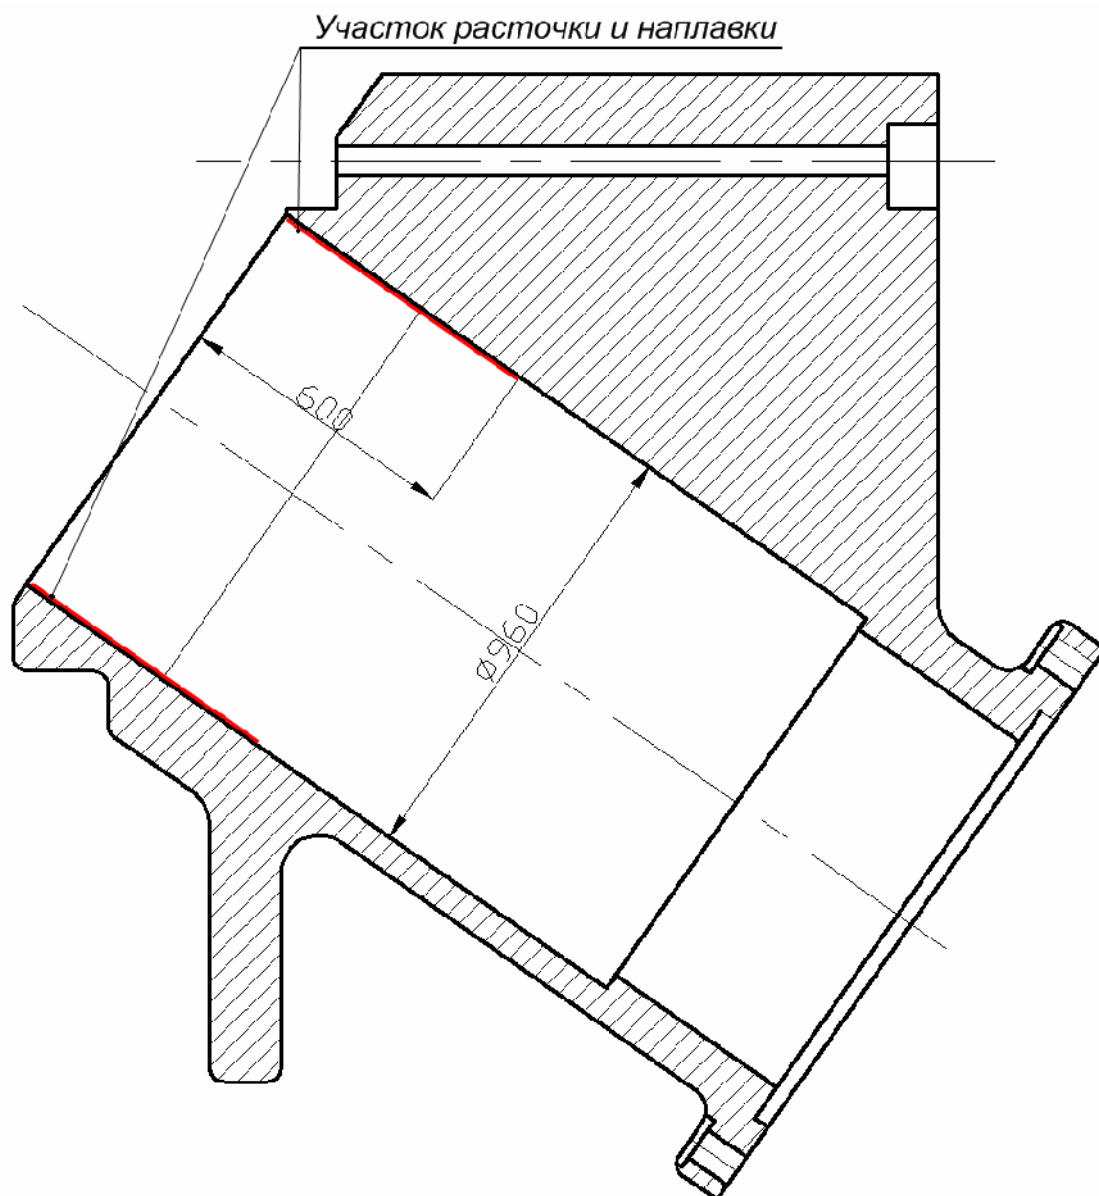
Схема расположения цилиндрического отверстия с поврежденной поверхностью в станине прокатного стана
